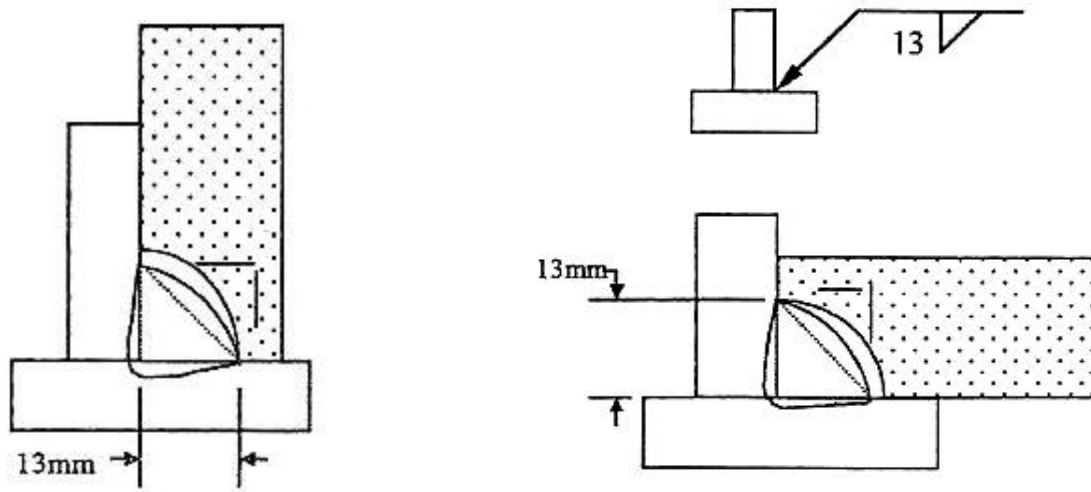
Medición de una soldadura de filete convexa
